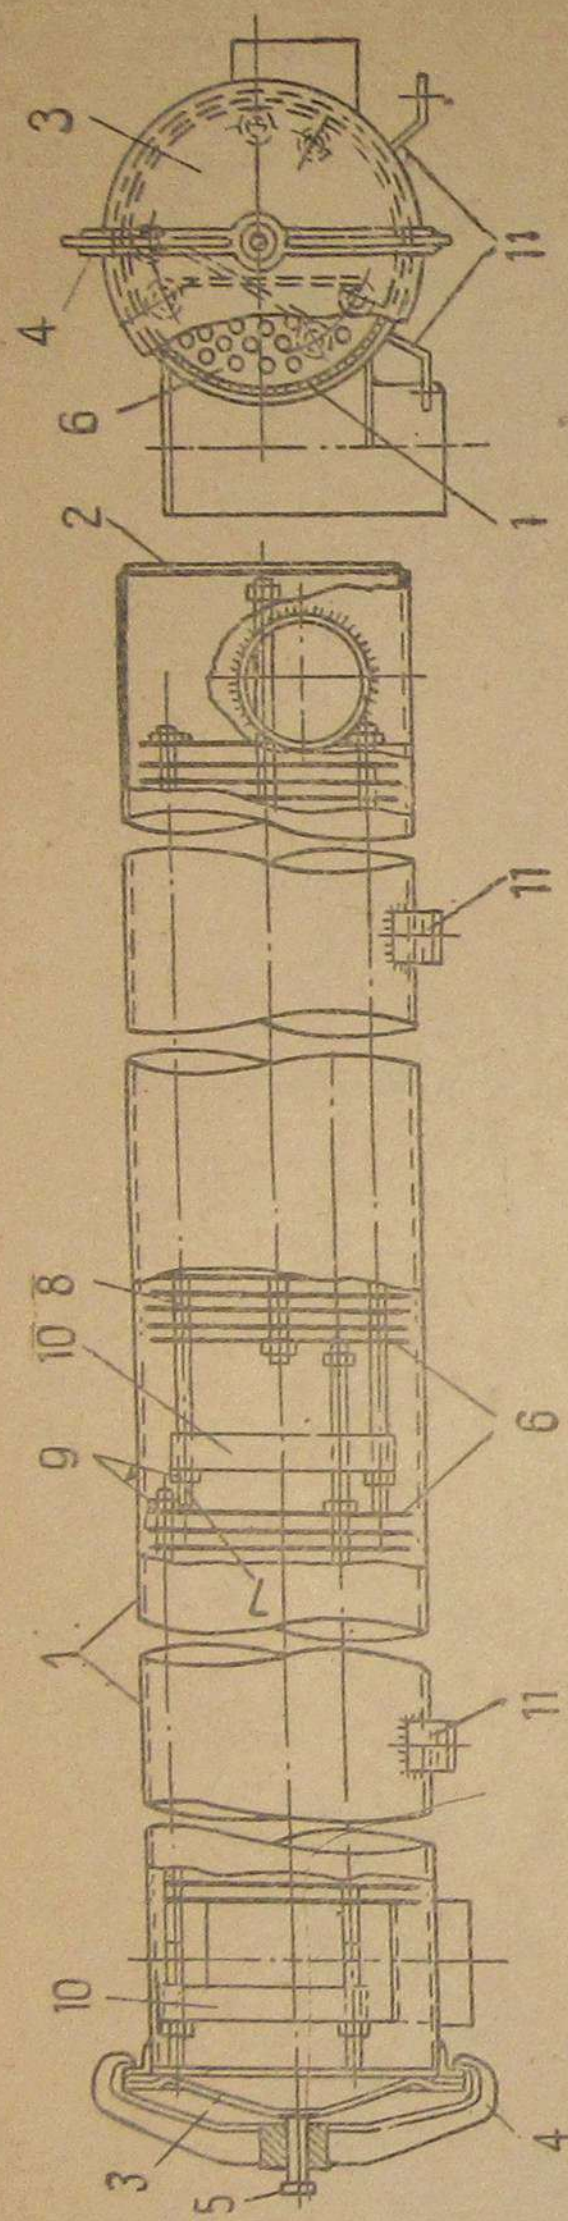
Горизонтальный очиститель грубой очистки газа установки ЗИС-21:
